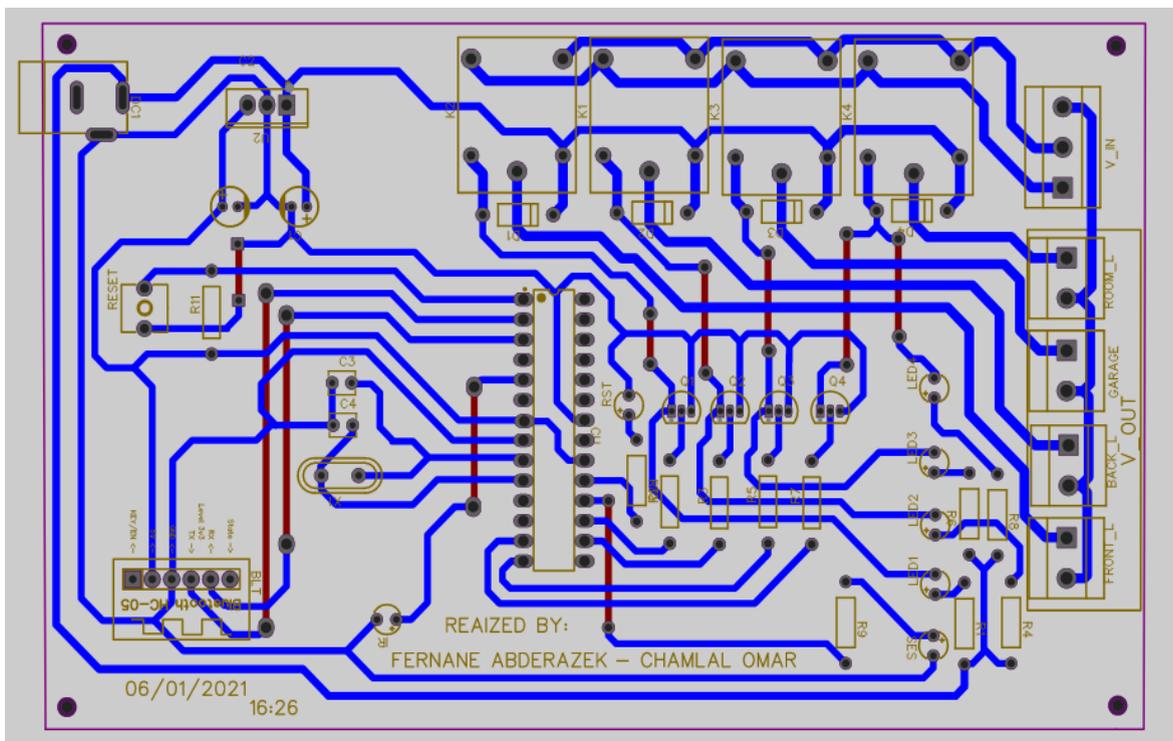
Carte PCB avec un Arrière-plan Gris
